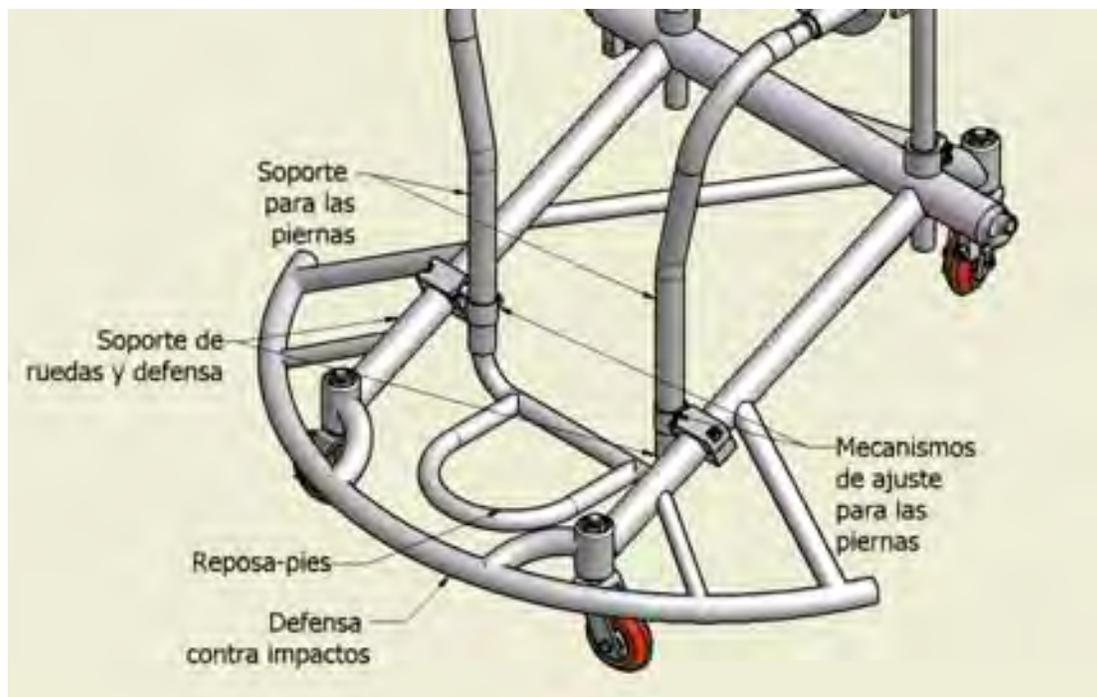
En esta imagen se observa la posición del mecanismo de ajuste para las piernas y otras partes de la silla que están involucradas.
